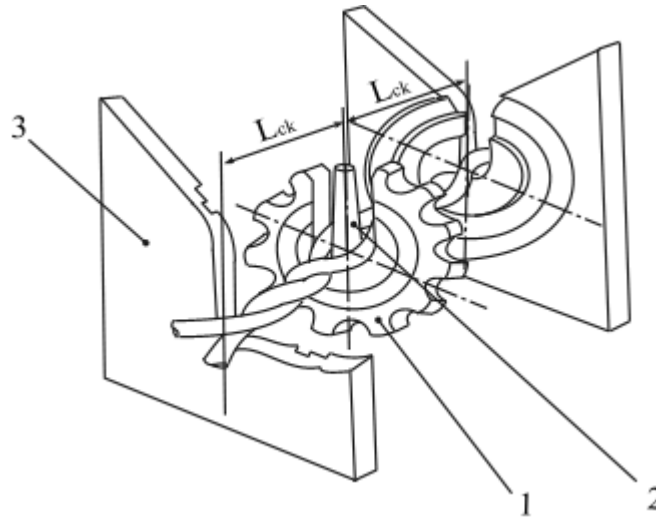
Схема скручуючого вузла: 1 – скручуюча шестерня; 2 – палець; 3 – корпус
